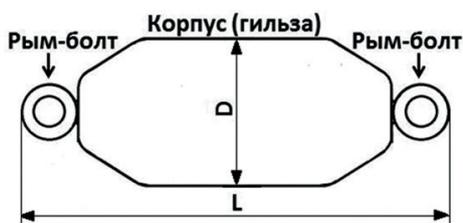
Внешний вид, детали и размеры пробного цилиндра для полимерных труб.
